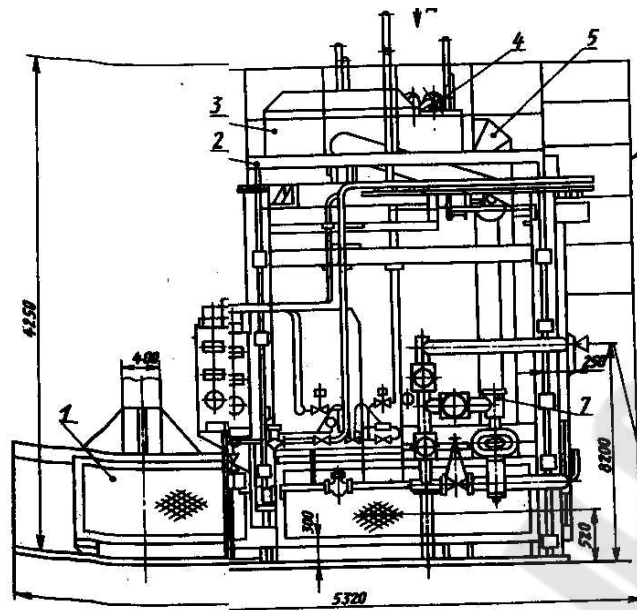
Установка подогрева шихты, разработанная Институтом газа АН УССР: 1 – кожух отбора продуктов горения; 2 – площадка обслуживания; 3 – камера сжигания газа; 4 – газовая горелка; 5 – трубопровод подачи воздуха
